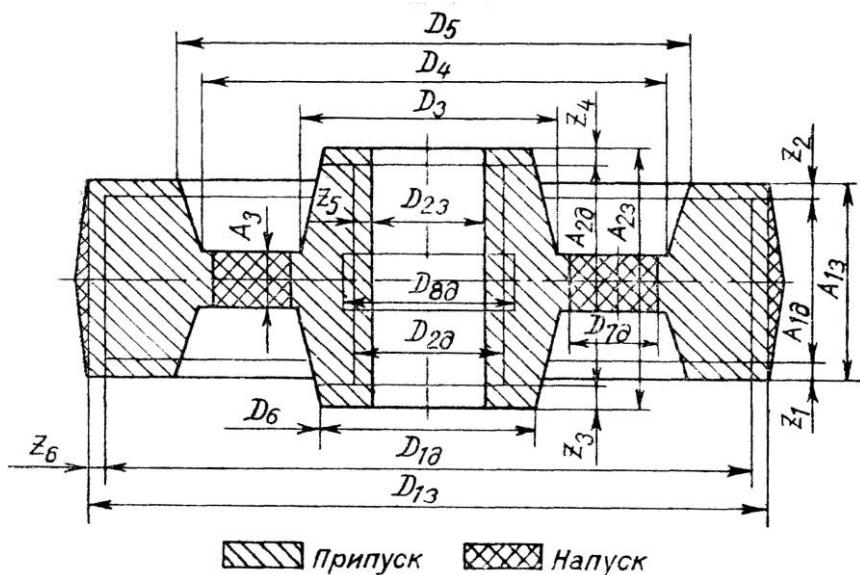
Заготовка шестерні. Розміри, напуски та припуски на обробку різанням.
